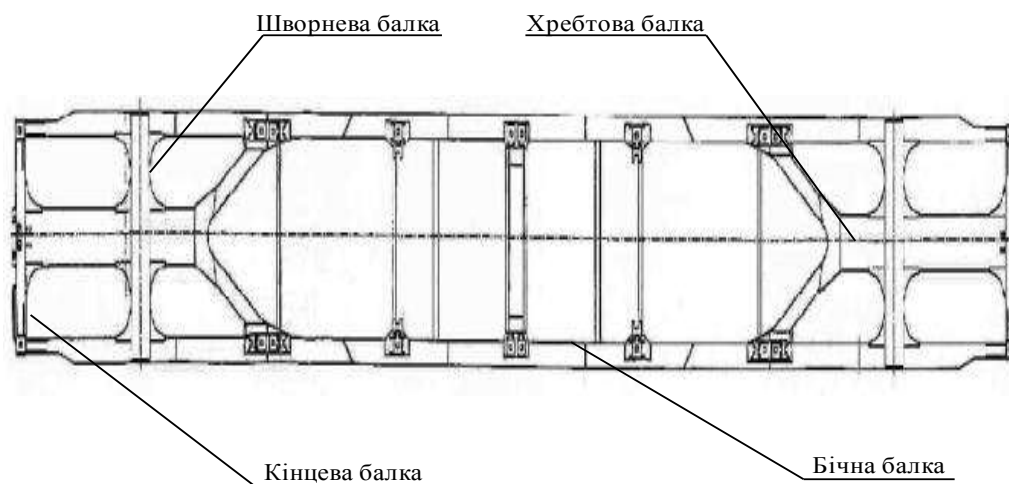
Загальний вид довгобазного вагона-платформи
